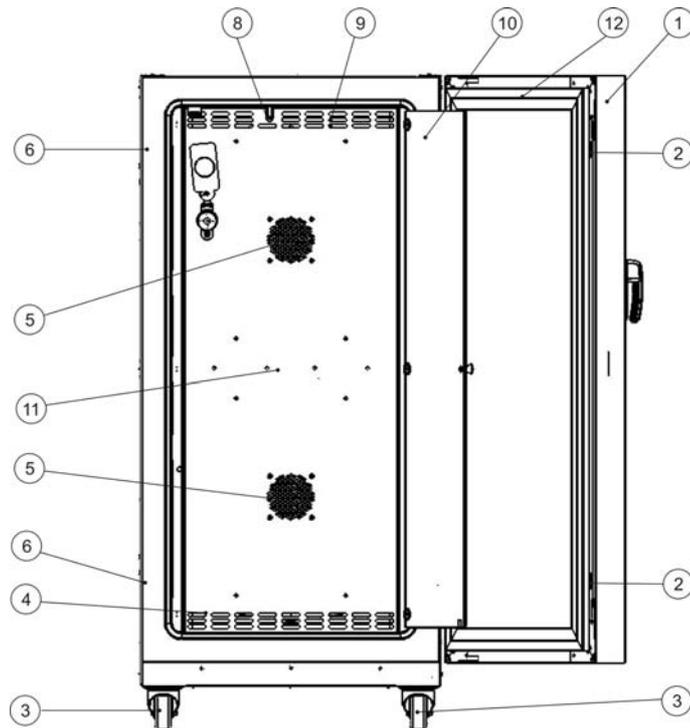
Frontansicht Kühlinkubator IMP 400
